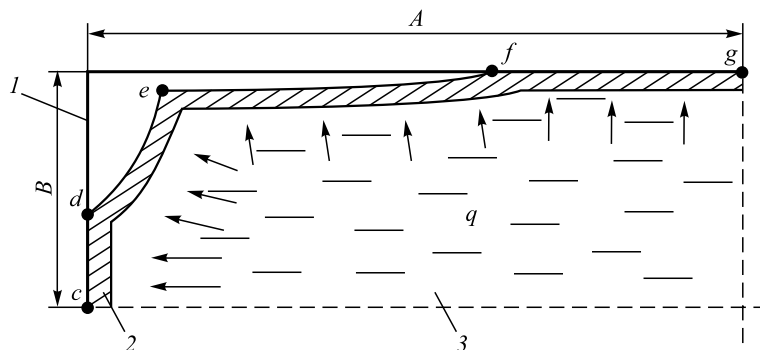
Схема зазора в углу кристаллизатора между оболочкой слябовой заготовки и стенками кристаллизатора:
